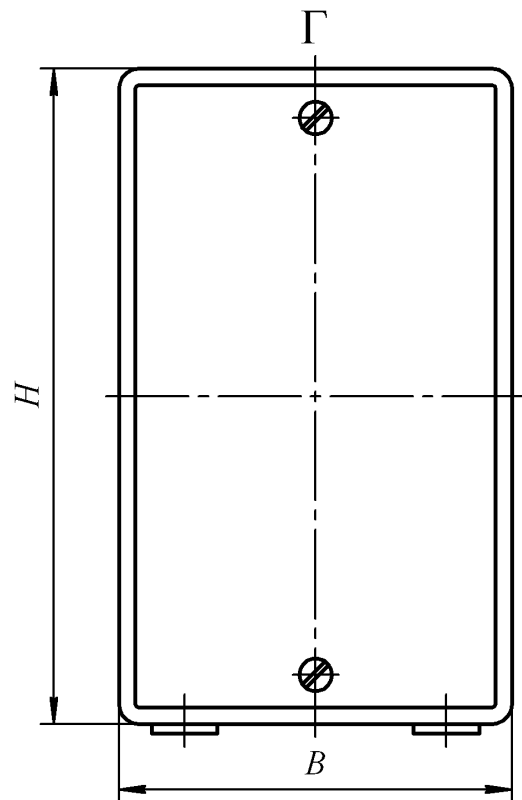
, б – Корпус (представитель ТНС РЭС)
